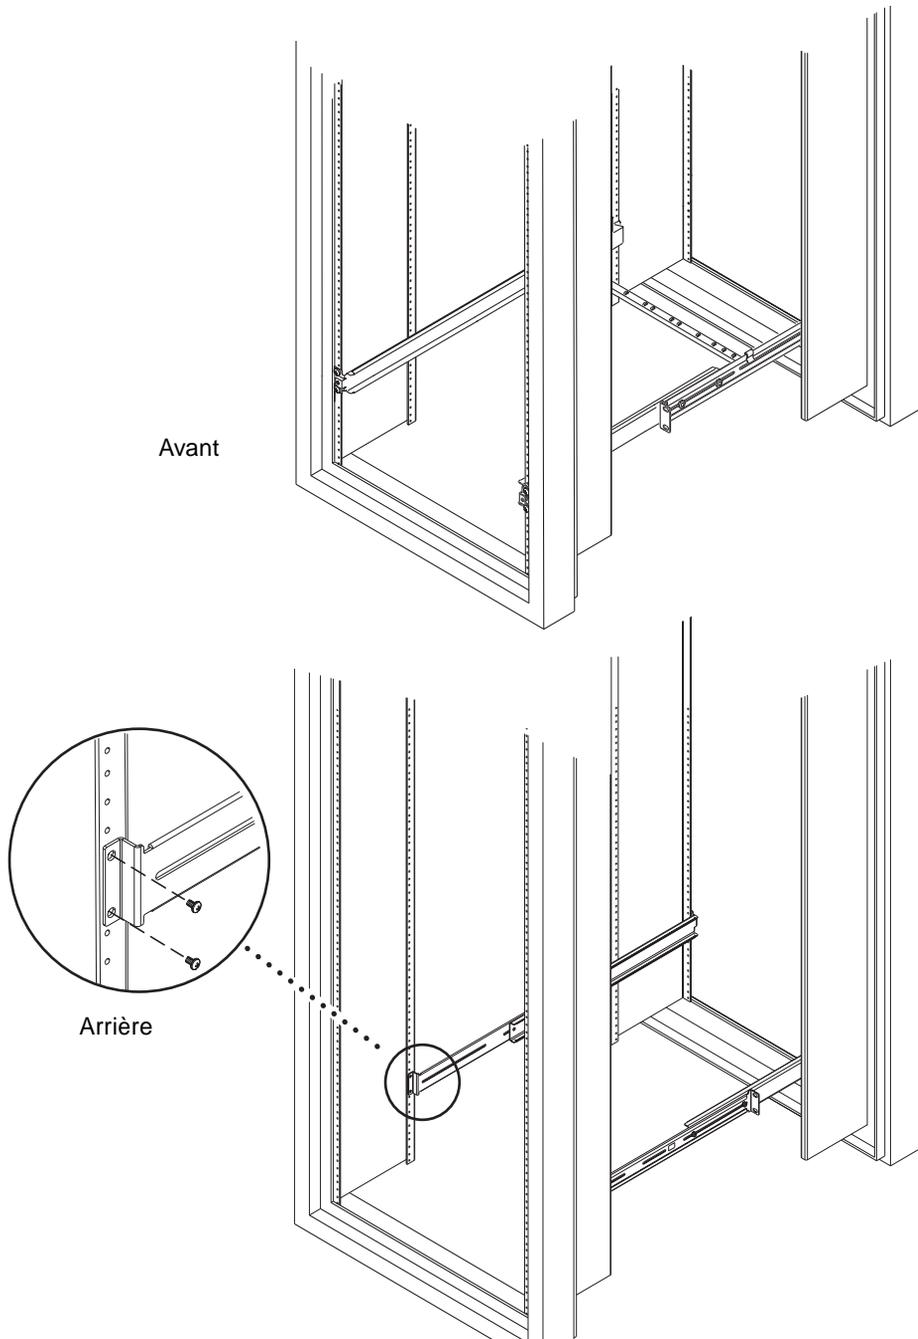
Fixation des glissières sur une armoire Sun StorEdge de 72 pouces de hauteur, vues avant et arrière (les panneaux latéraux ont été retirés par souci de clarté)
